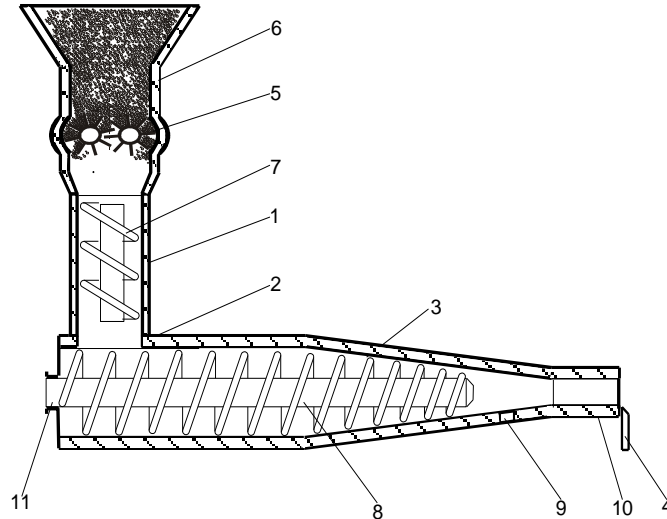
Схема установки для формування паливних матеріалів: 1 – завантажувальний бункер; 2 – циліндрична частина корпусу; 3 – конічна частина корпусу; 4 – ріжучий пристрій; 5 – дозуючий пристрій; 6 – підготовча камера; 7 – дозуючий шнек; 8 – шнек із транспортуючими, ущільнюючими та витискаючими лопатками; 9 – дренажний отвір; 10 – фільтр; 11 – вал редуктора
